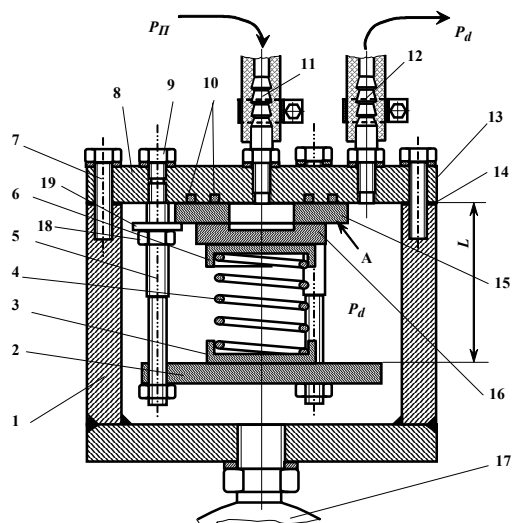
Приспособление для крепления элементов щели: 1–корпус, 2–прижимной диск, 3–нижний стакан пружины, 4–тарированная пружина сжатия, 5–натяжные шпильки, 6–верхний стакан пружины, 7–болты крепления крышки, 9–заглушка, 10–эластичные уплотнительные кольца, 11–штуцер подвода давления, 12–штуцер отвода газа, 13–крышка, 14–прокладка, 15–большой диск, 16–малый диск, 17–манометр для измерения давления P_d , 18 и 19–гайка и шайба крепления диска 15, A – свободная поверхность для контроля направления потока
